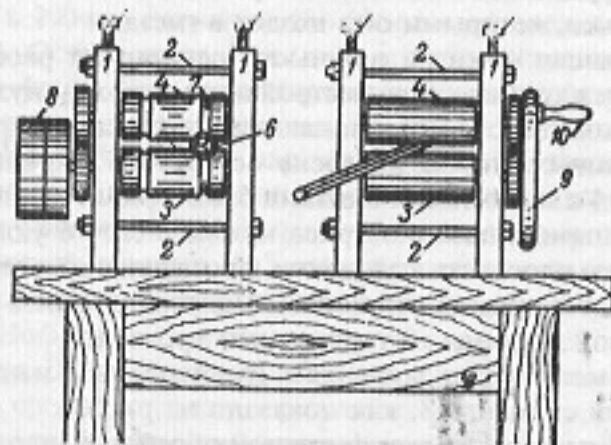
Механический станок для раскалывания и строжки прута — шиф:
